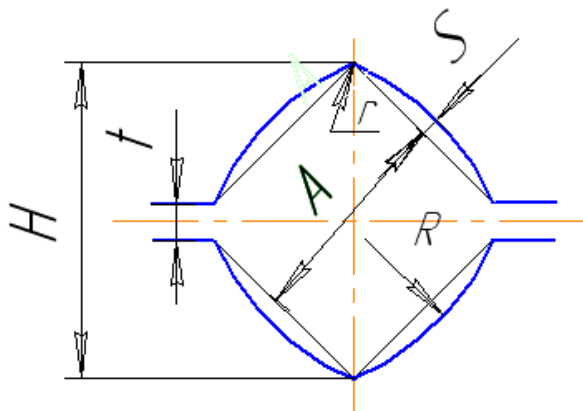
Предовальный стрельчатый квадратный калибр по схеме 6
